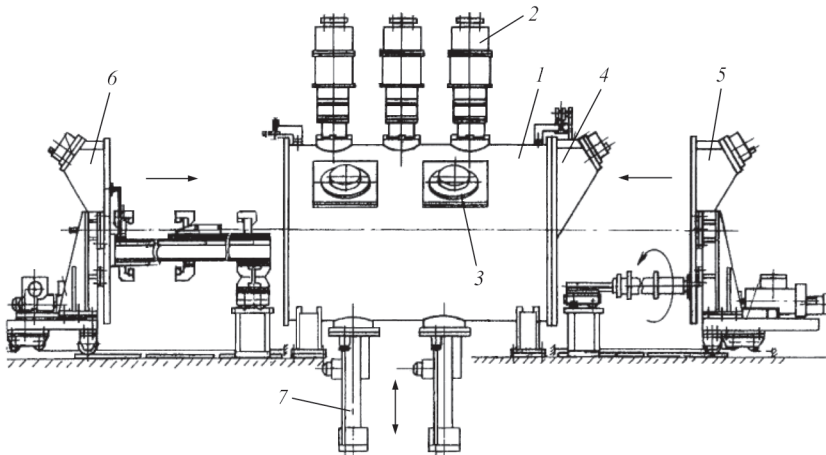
Технологічна схема спеціалізованої електронно-променевої установки для оплавлення зливків: 1 — камера оплавлення; 2 — електронно-променева гармата; 3 — система спостереження; 4 — кришка; 5 — механізм обертання та пересування циліндричних зливків; 6 — механізм обертання та пересування зливків прямокутного перерізу; 7 — механізм вертикального пересування
